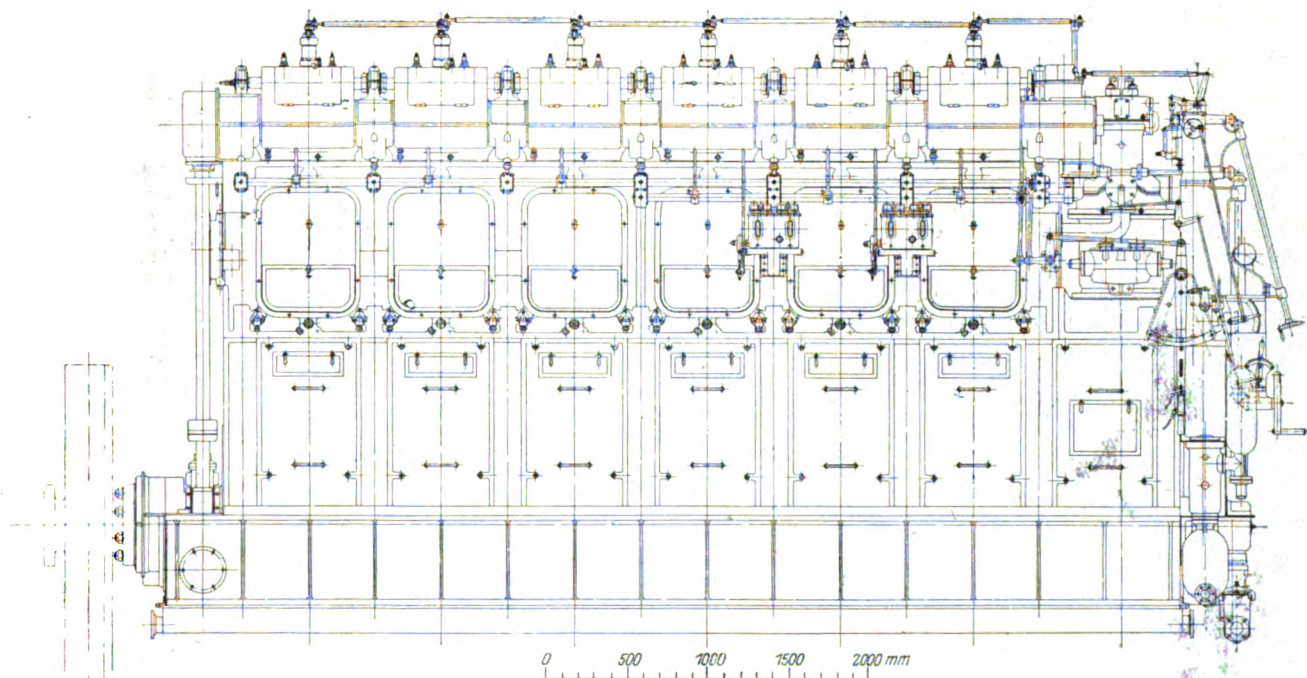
M. A. N.-Dieselmotor mit Tauchkolben
